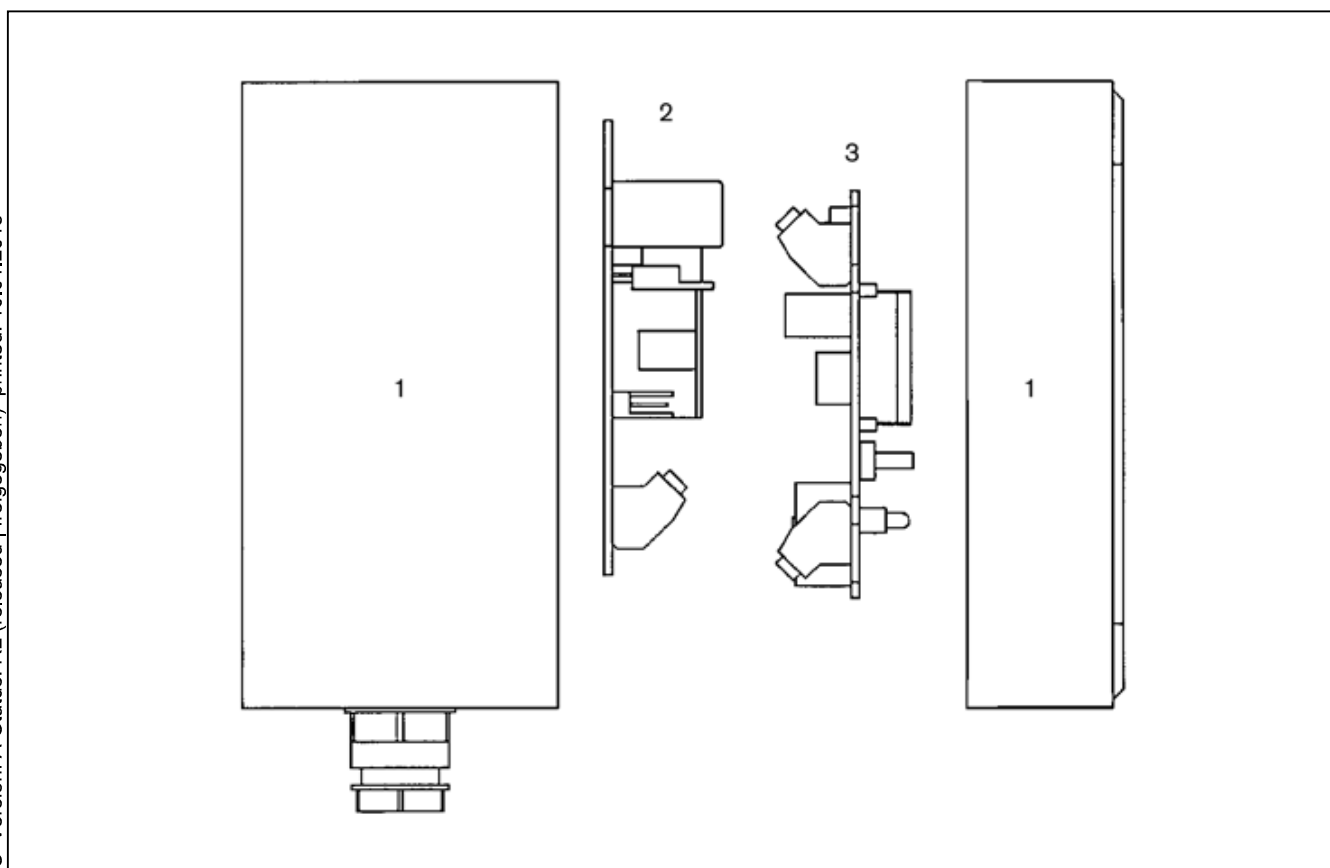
Despiece de los repuestos del Tipo 8025 universal en versión de montaje en panel
